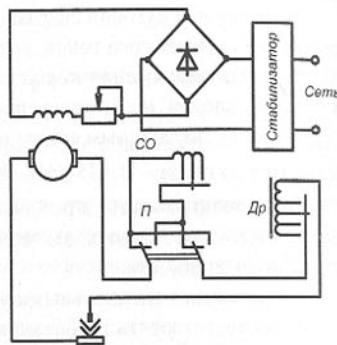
Схема универсального сварочного генератора
